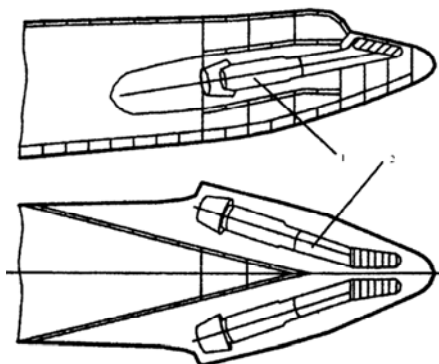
Схема установки носовых двигателей в корпусе:
